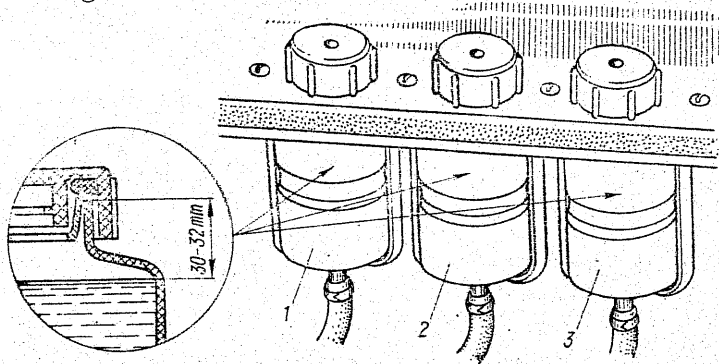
Ausgleichbehälter des Hauptbremszylinders und des Hauptkupplungsausrückzylinder. (Ansicht auf die Behälter von der Kofferraumseite):
